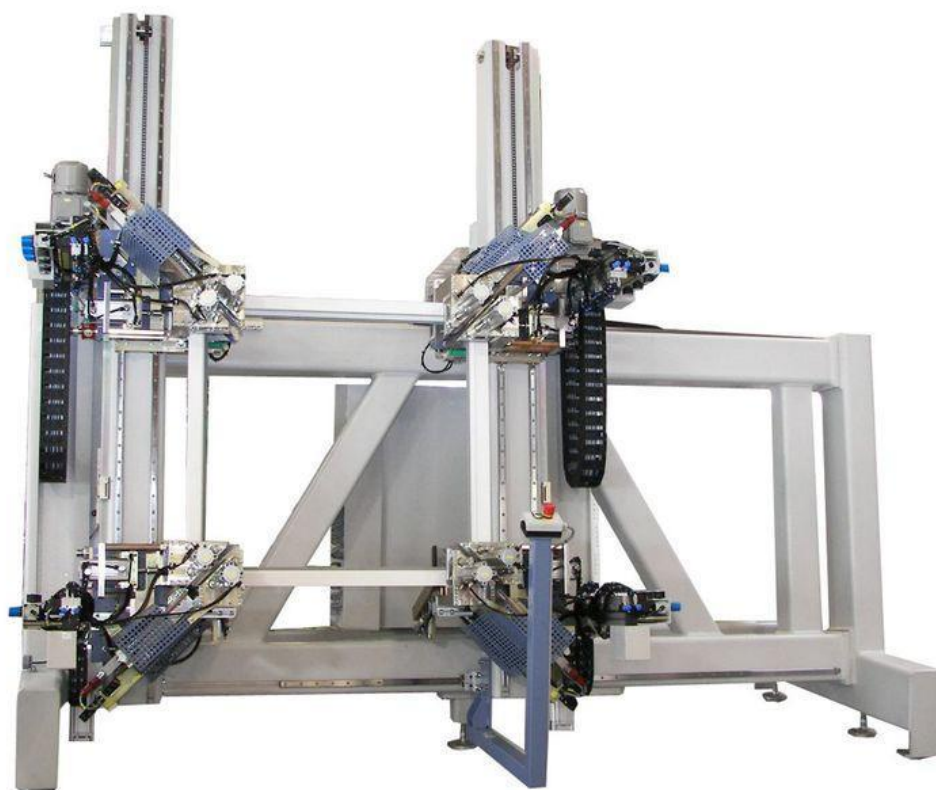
Вертикальная сварочная установка STURTZ SE-VSM 30/26P Compact⁶
